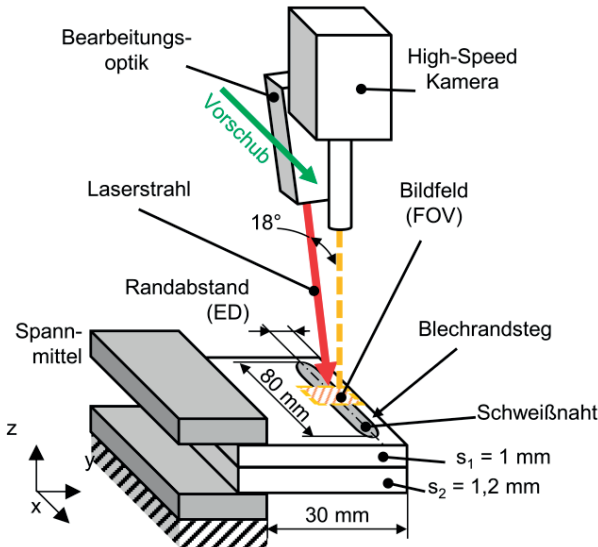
Skizze des Versuchsaufbaus zur Bestimmung der thermomechanischen Verformung von Schweißnähten in Randnähe. [53]
